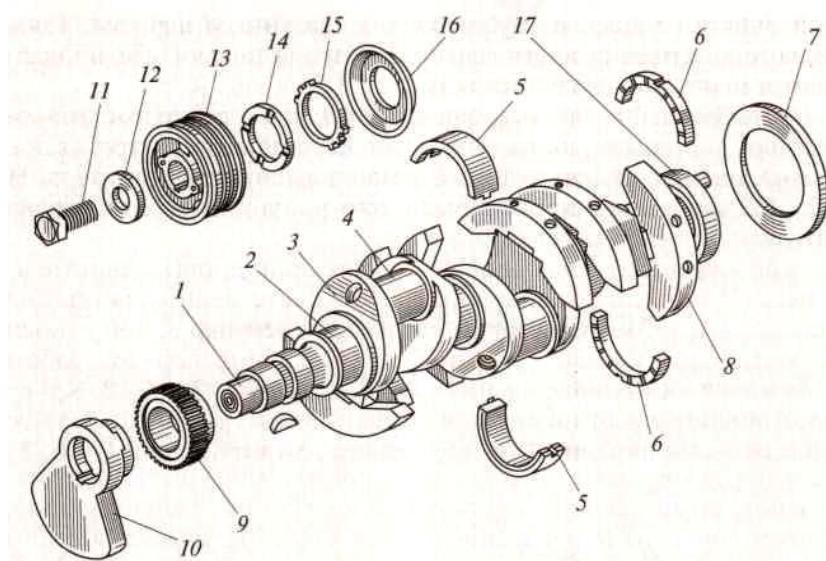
Коленчатый вал двигателя ЯМЗ-236:
